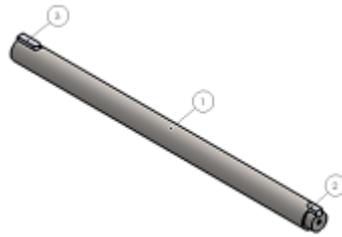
4 Sistem Transmisi Mesin Pencacah dan Penepung Bahan Baku Pakan Ternak Dengan Penggerak Motor Bensin
